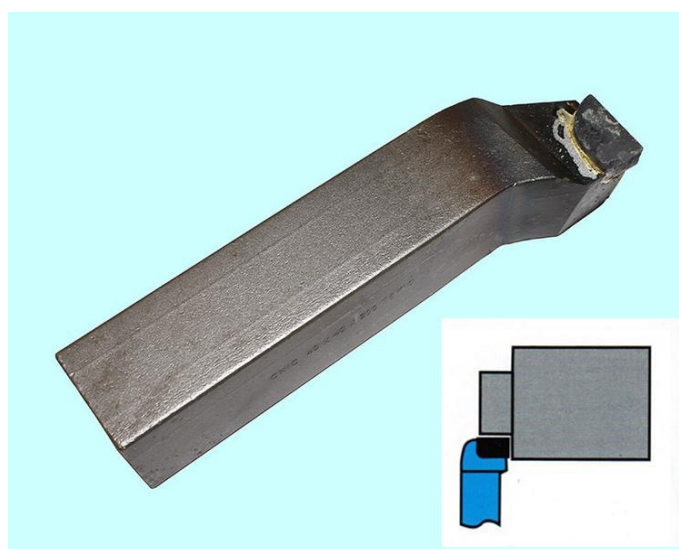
Резец подрезной отогнутый 40x40x200 ВК8 DIN 4977 "CNIC"
